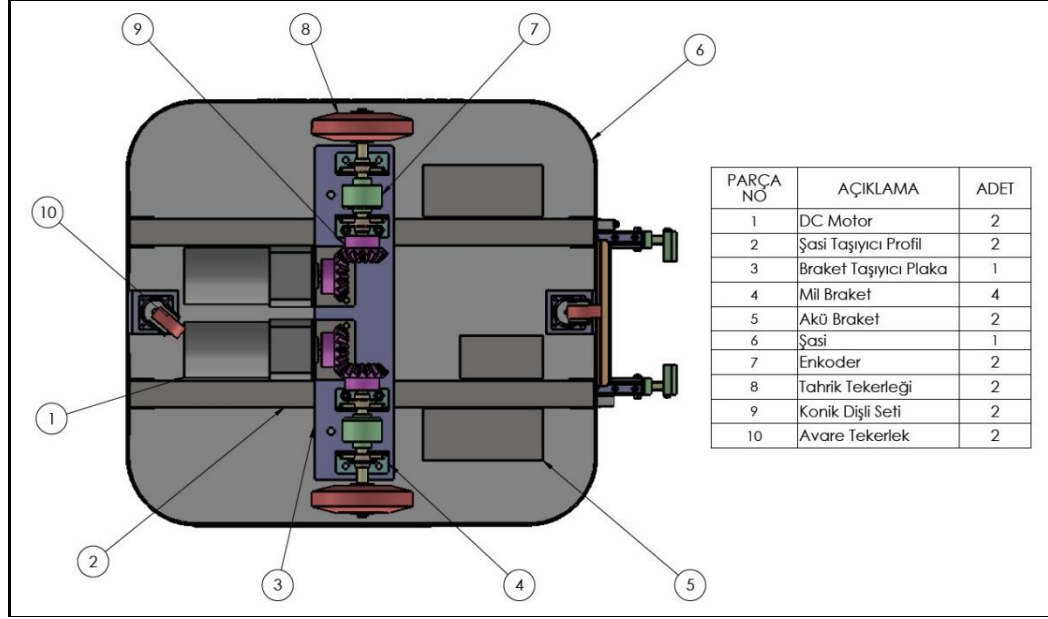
Mobil Depo Robotunun Alt Komponentleri
